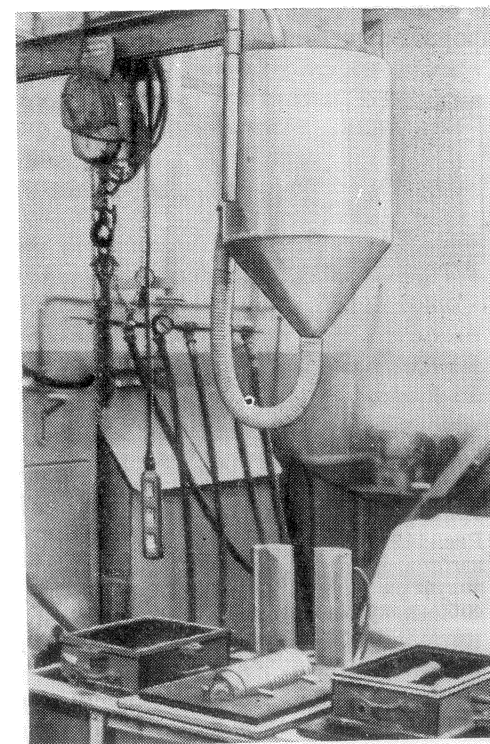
Общий вид модельно-опочной оснастки для формовки из сыпучих песков гильз двигателя СМД-14.
